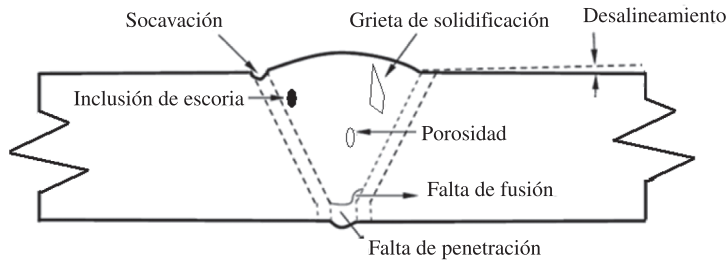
Imperfecciones de soldadura en juntas a tope. Adaptada de [15].
